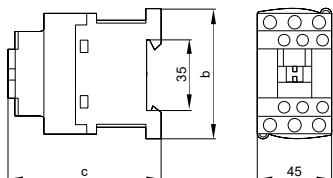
Габаритные размеры контакторов КМИ-А-10612–КМИ-А-11812 / Figure 1 — Overall dimensions of contactors KMI-A-10612–KMI-A-11812
